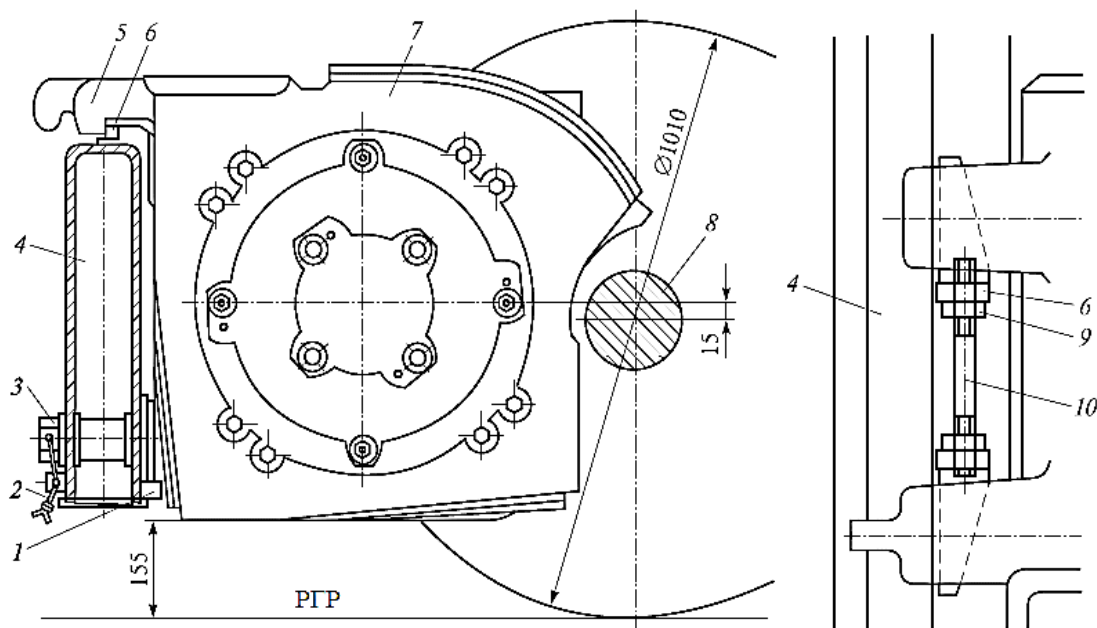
Схема рамної підвіски тягового двигуна:
